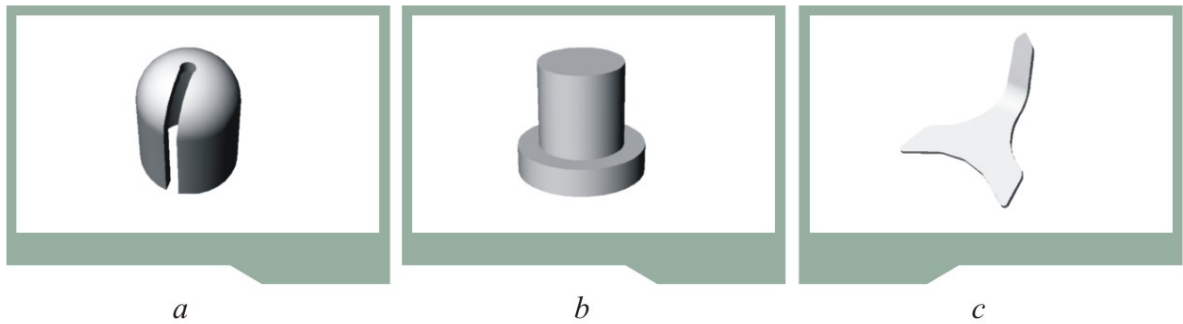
a) pasador guaya b) pasador de tornillos del porta termo c) spoiler
